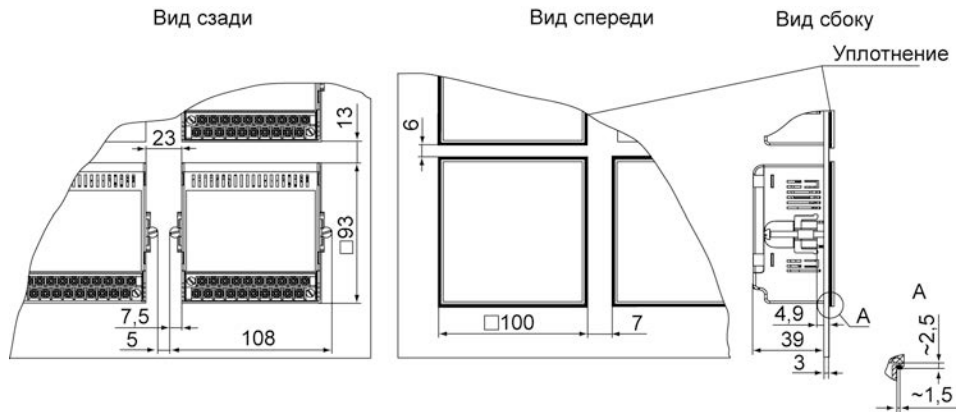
Прибор в корпусе Щ11, установленный в щит толщиной 3 мм
